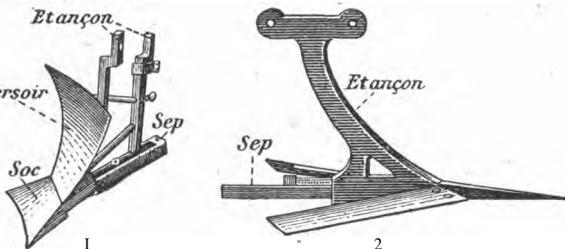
Étançons formant corps de charrue. 1. En deux pièces ; 2. D'une seule pièce.
